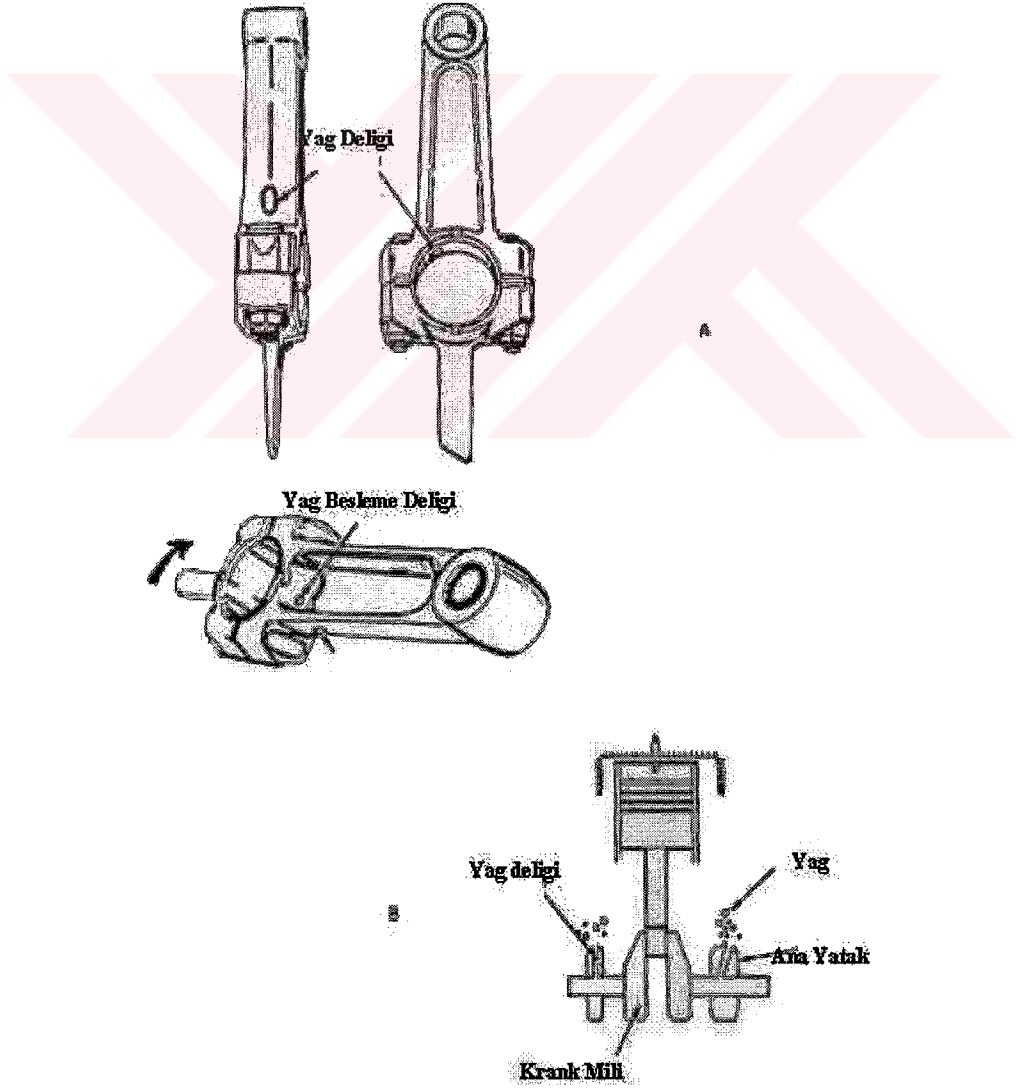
Biyel uygulaması (Miller & Miller, 1993)
